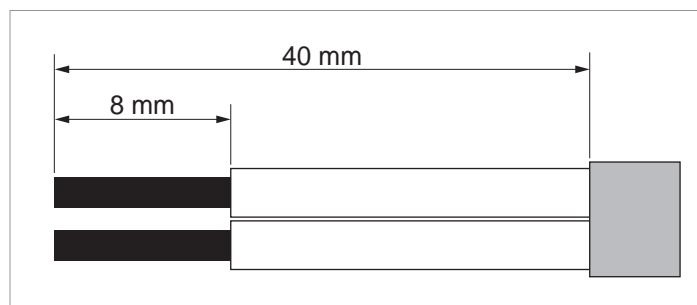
Assemblage du câble de la fiche multicontact
